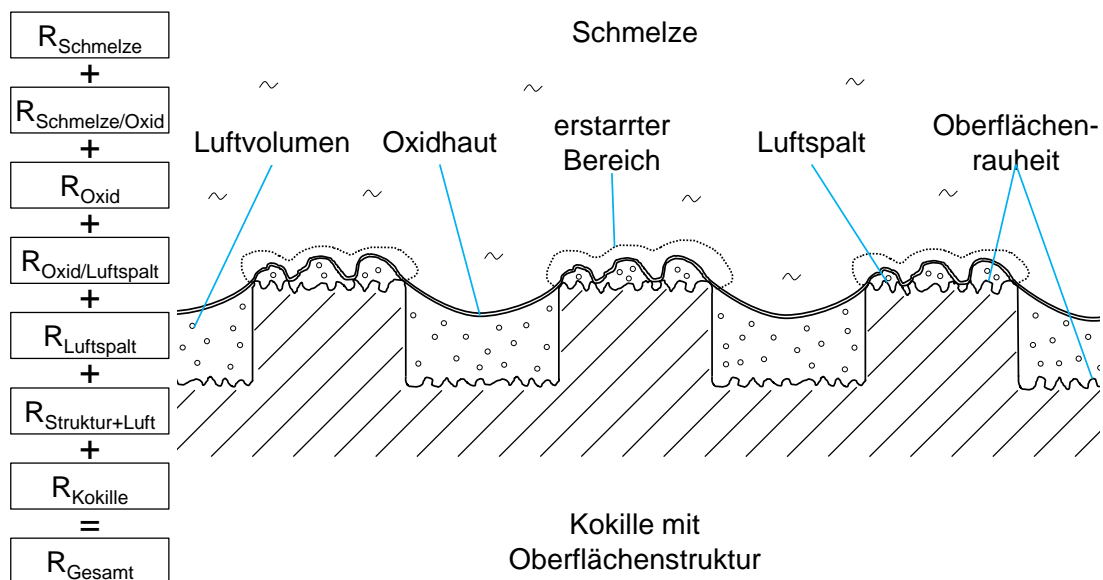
Visualisierung einer mit Schmelze benetzten, oberflächenstrukturierten Kokille
